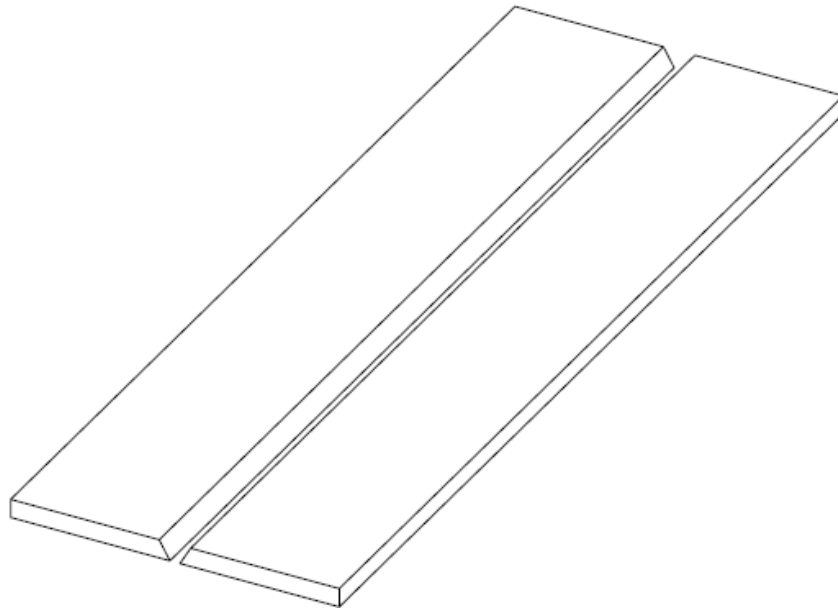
Esquema en 3D de las placas para obtener las juntas a soldar.
